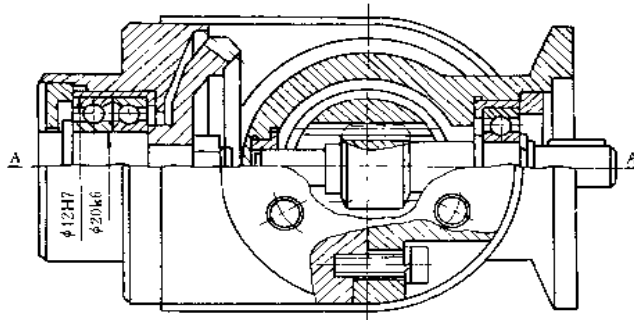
工业机器人操作机手腕摆动机构轴承配置
